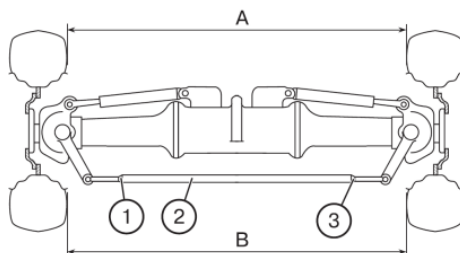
Схема проверки и регулировки угла схождения управляемых колес
